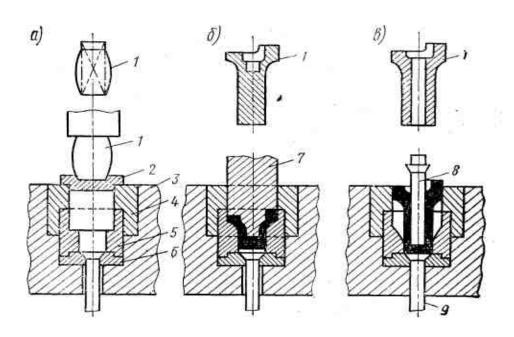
Схема штампа гидравлического пресса для изготовления поковки втулки с применением накладного кольца и сменных пуансонов: а, б, в – соответственно I, II и III – переходы: 1 – заготовка и поковка по переходам; 2 – осадочная плита; 3 – матрица; 4, 5, 6 – вставки матрицы; 7 – формующий пуансон; 8 – прошивной пуансон; 9 – выталкиватель
